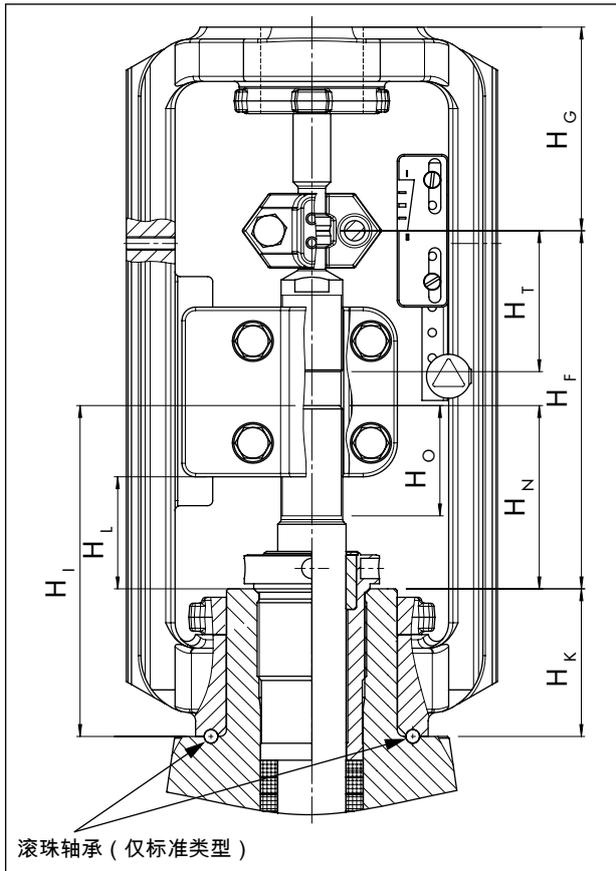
3271 型和 3277 型气动执行机构尺寸图, 含安装尺寸
